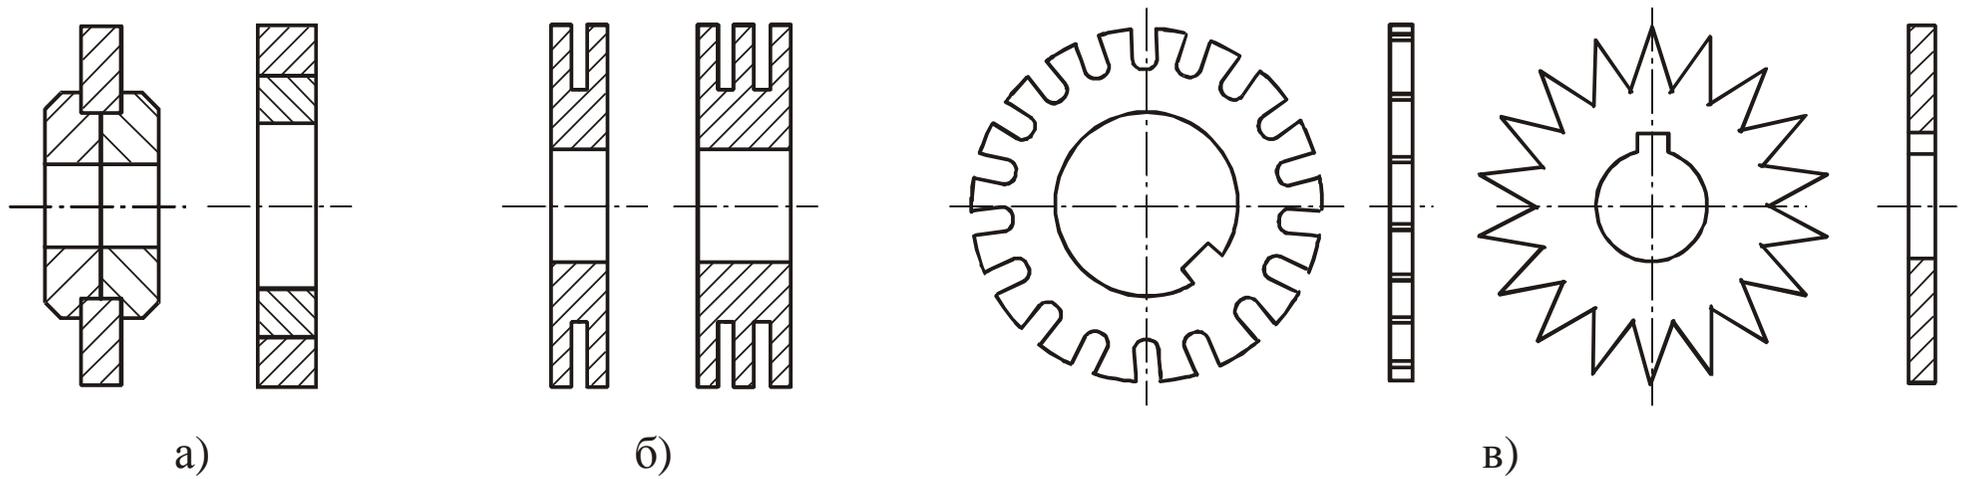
Инструменты для правки шлифовальных кругов методом обкатывания: *а* – твердосплавные ролики; *б* – стальные диски; *в* – тупозубая и острозубая звездочки
